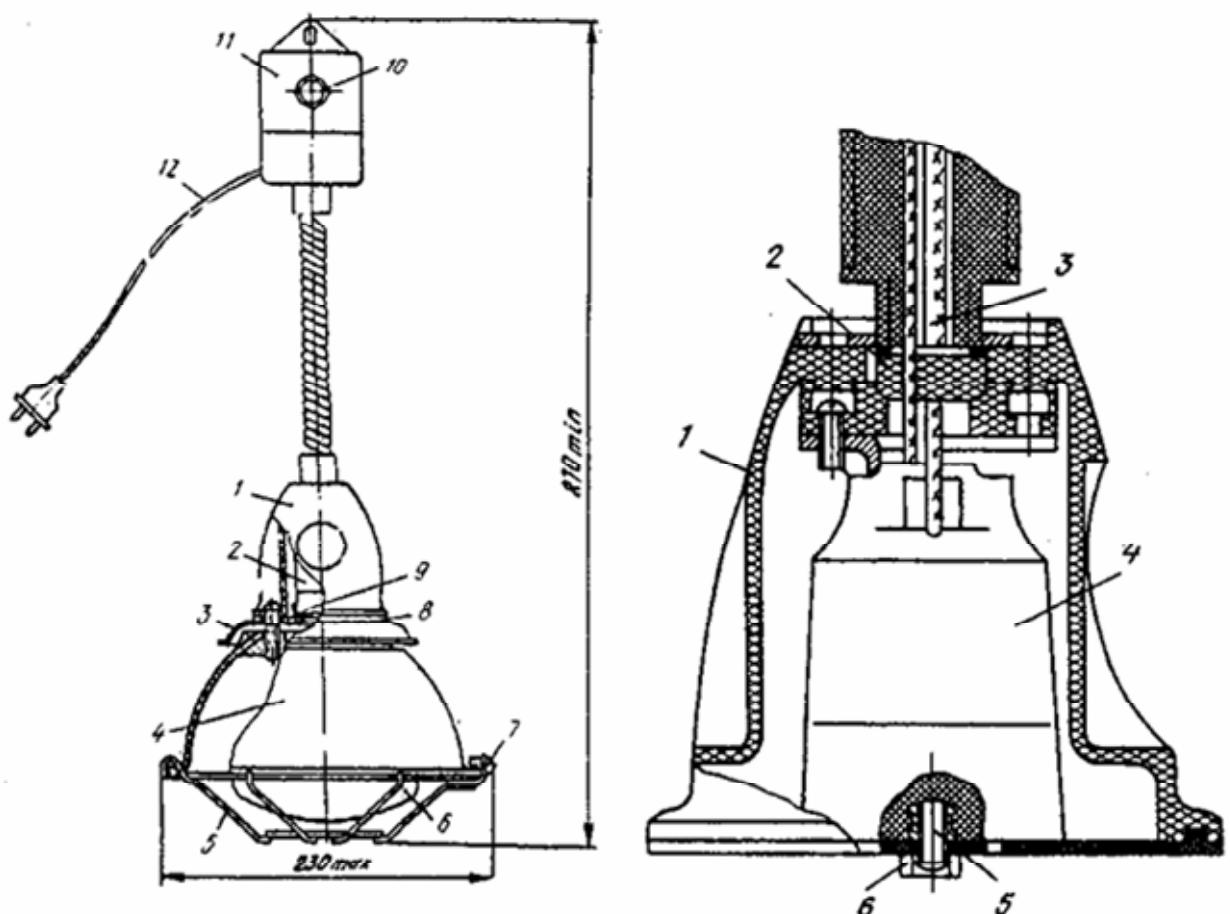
Общий вид и габаритные размеры облучателя "Вира" типа ССП06-250-001 У3,5
